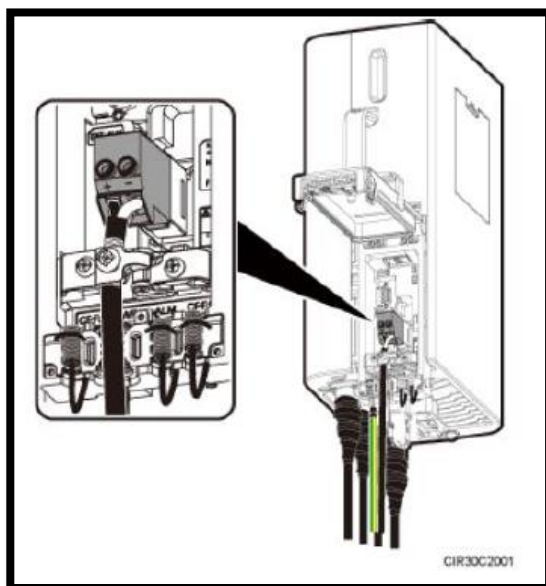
Posición conector pressfit en RRU, Site Santa Teresa
